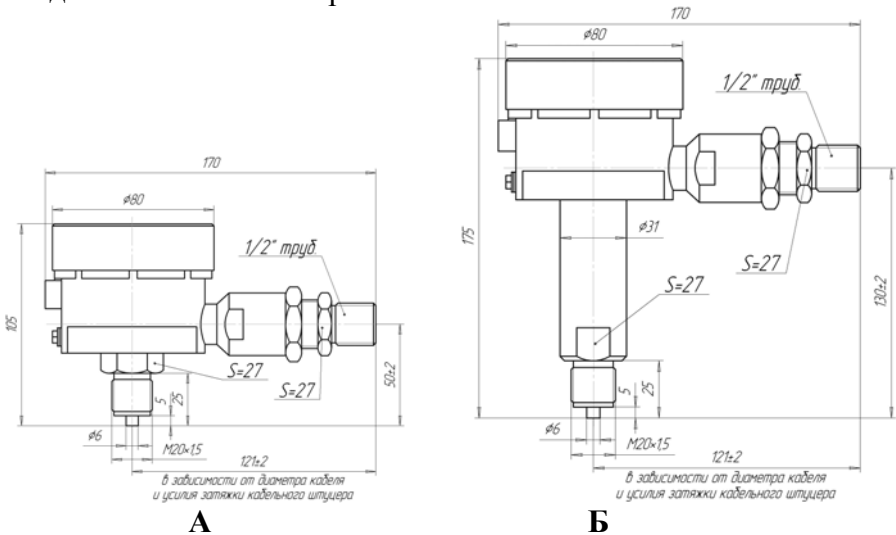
Модель 1205. Взрывозащита, стальной корпус, ввод под трубу.
